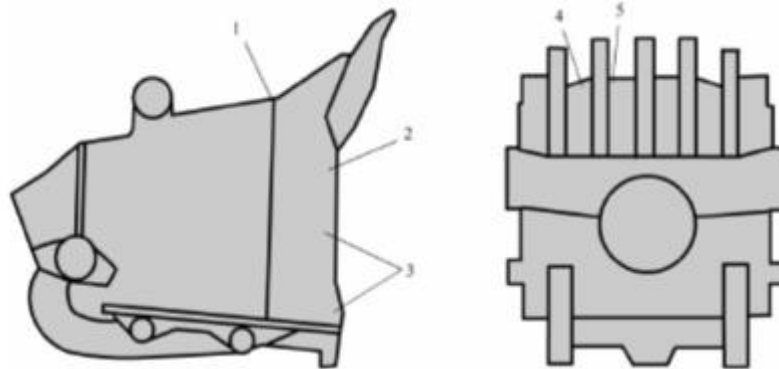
Крихкі руйнування корпусу ковша екскаватора
